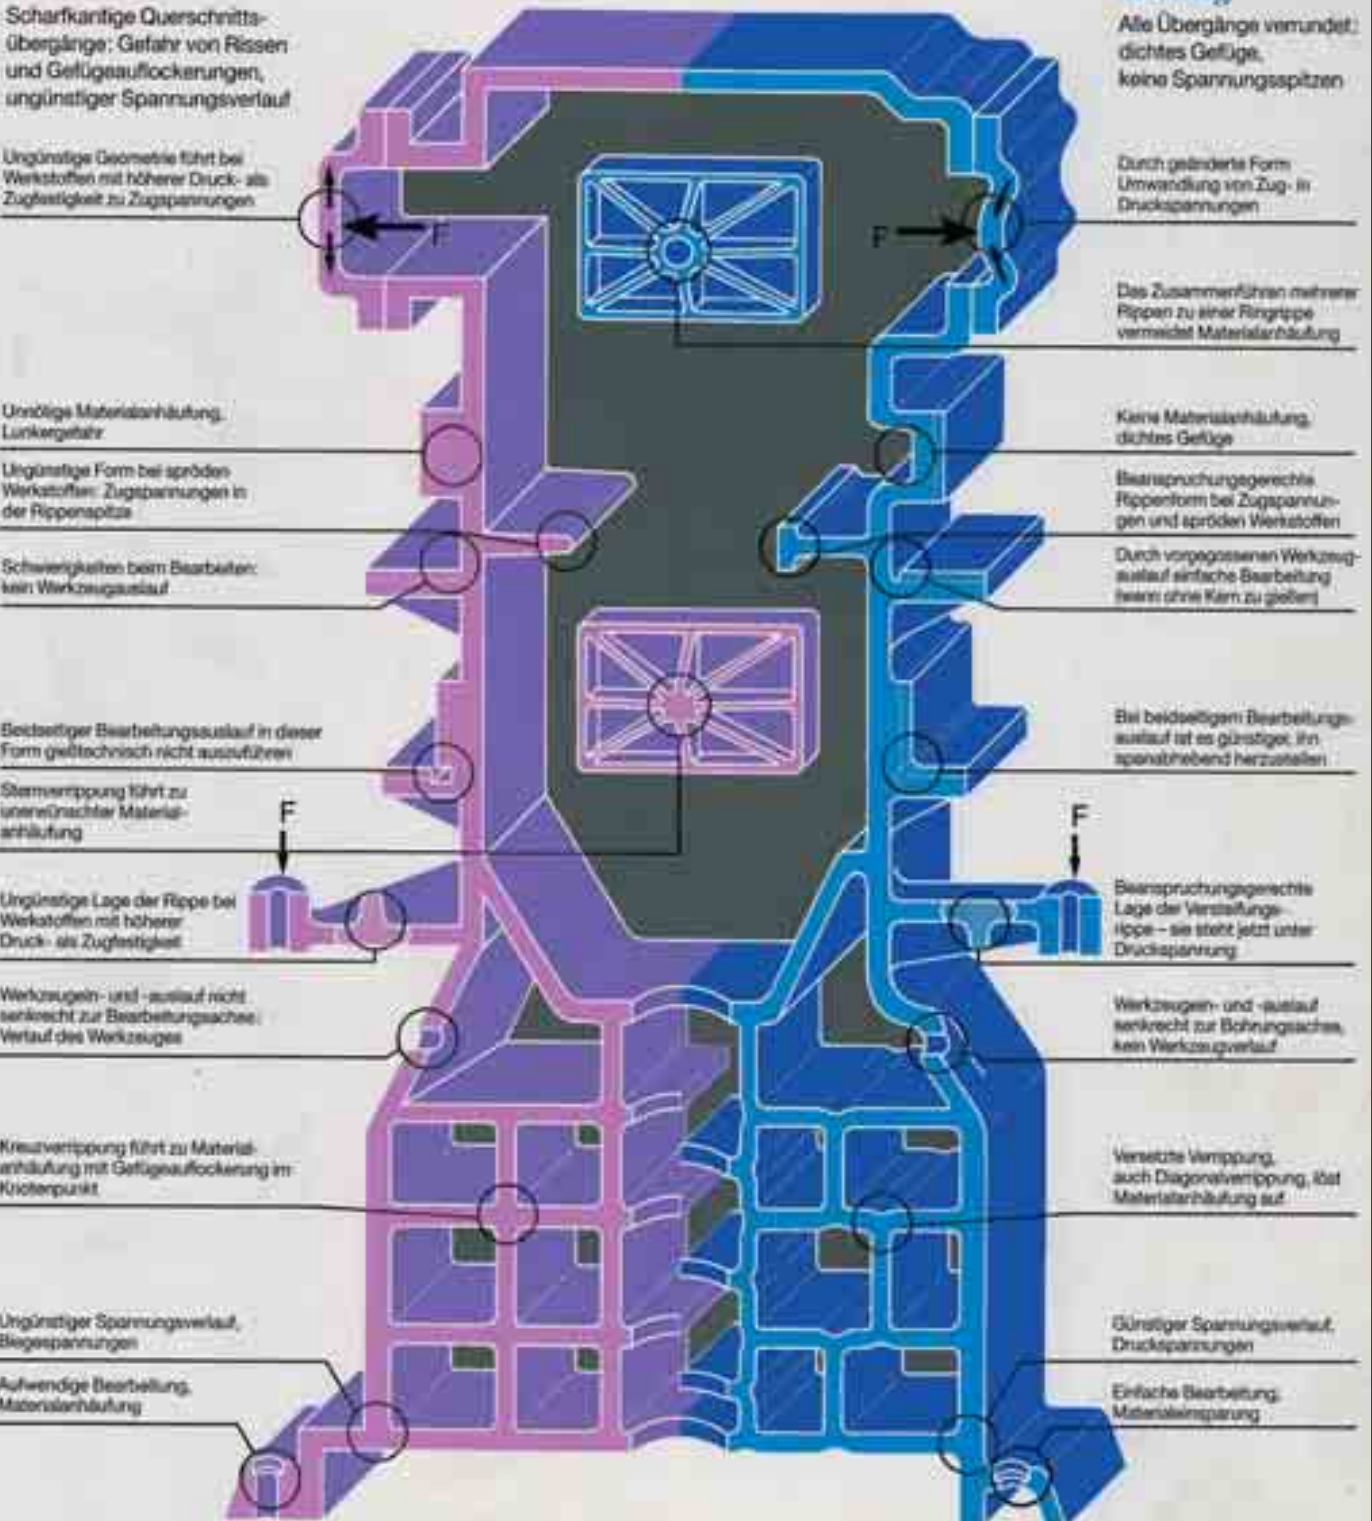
Wichtige Grundregeln zum gießgerechten Gestalten von Gussteilen links: fertigungstechnisch ungünstige Ausführung mit hohem Eigenspannungsanteil rechts: gießtechnisch angepasste, spannungsminimierte Ausführung.
